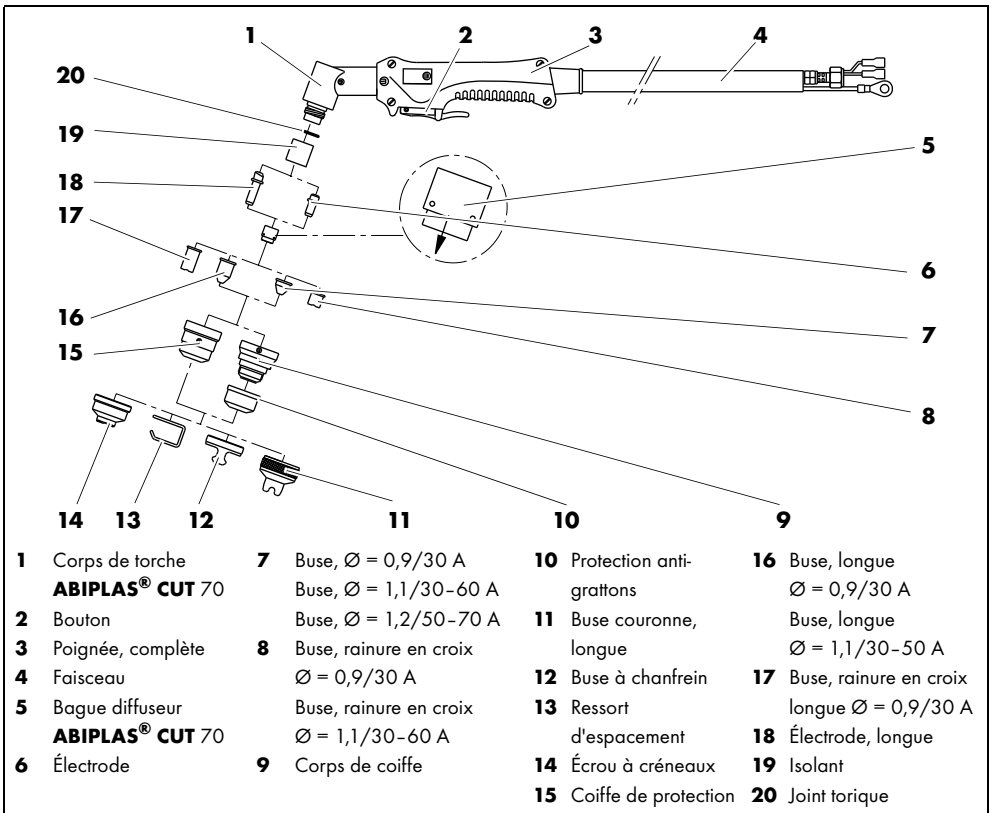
Vue d'ensemble de ABIPLAS® CUT 70
